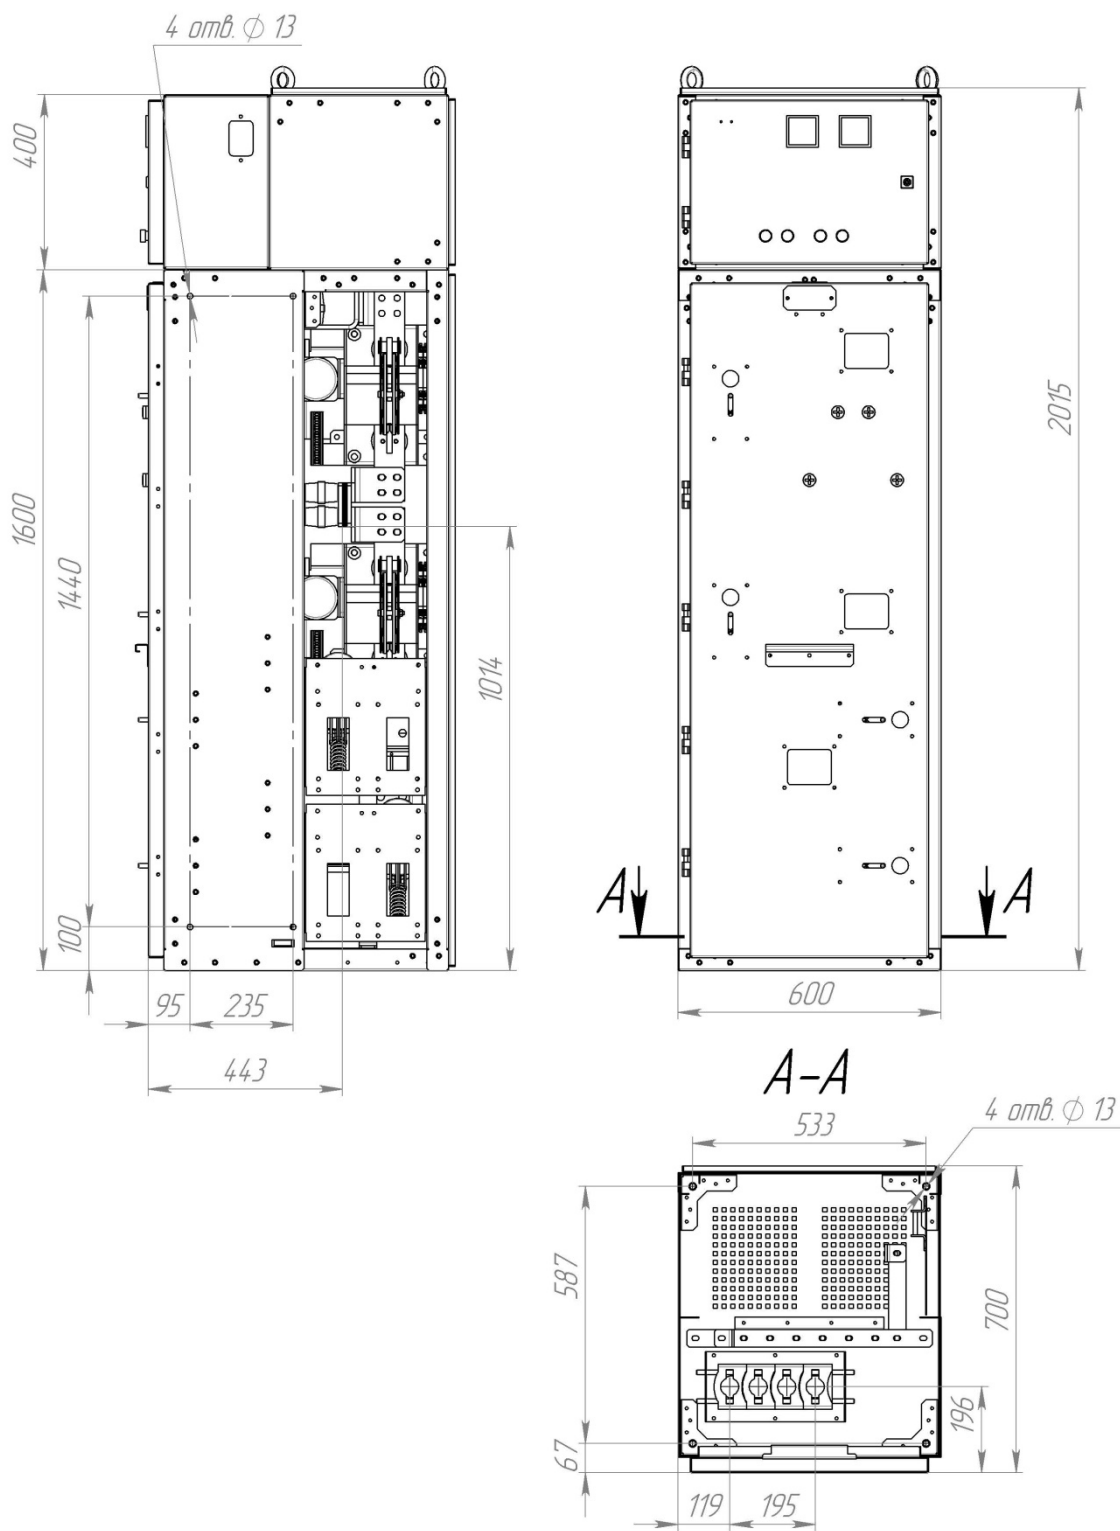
Габаритные и присоединительные размеры РУОШ-600
